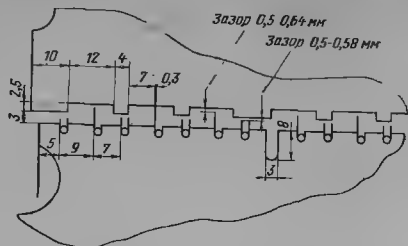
Крепление обоймы в корпусах турбин ЛМЗ
